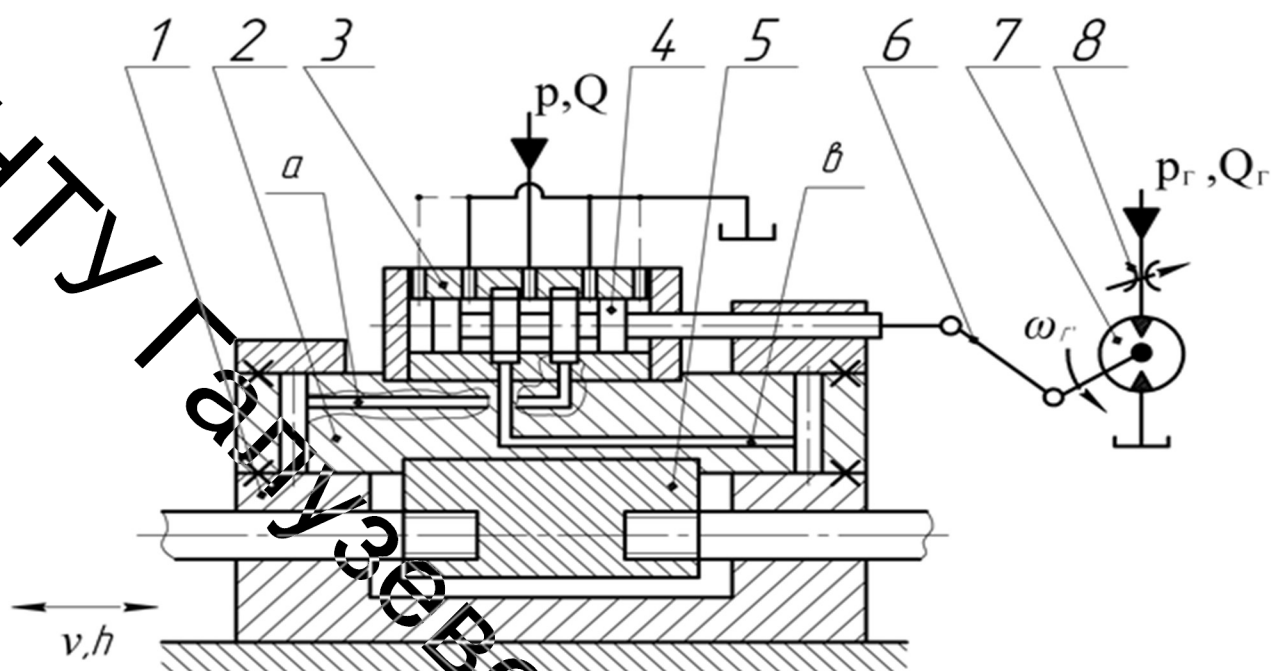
Конструктивна схема привода вібросупорта *ВГ-2
